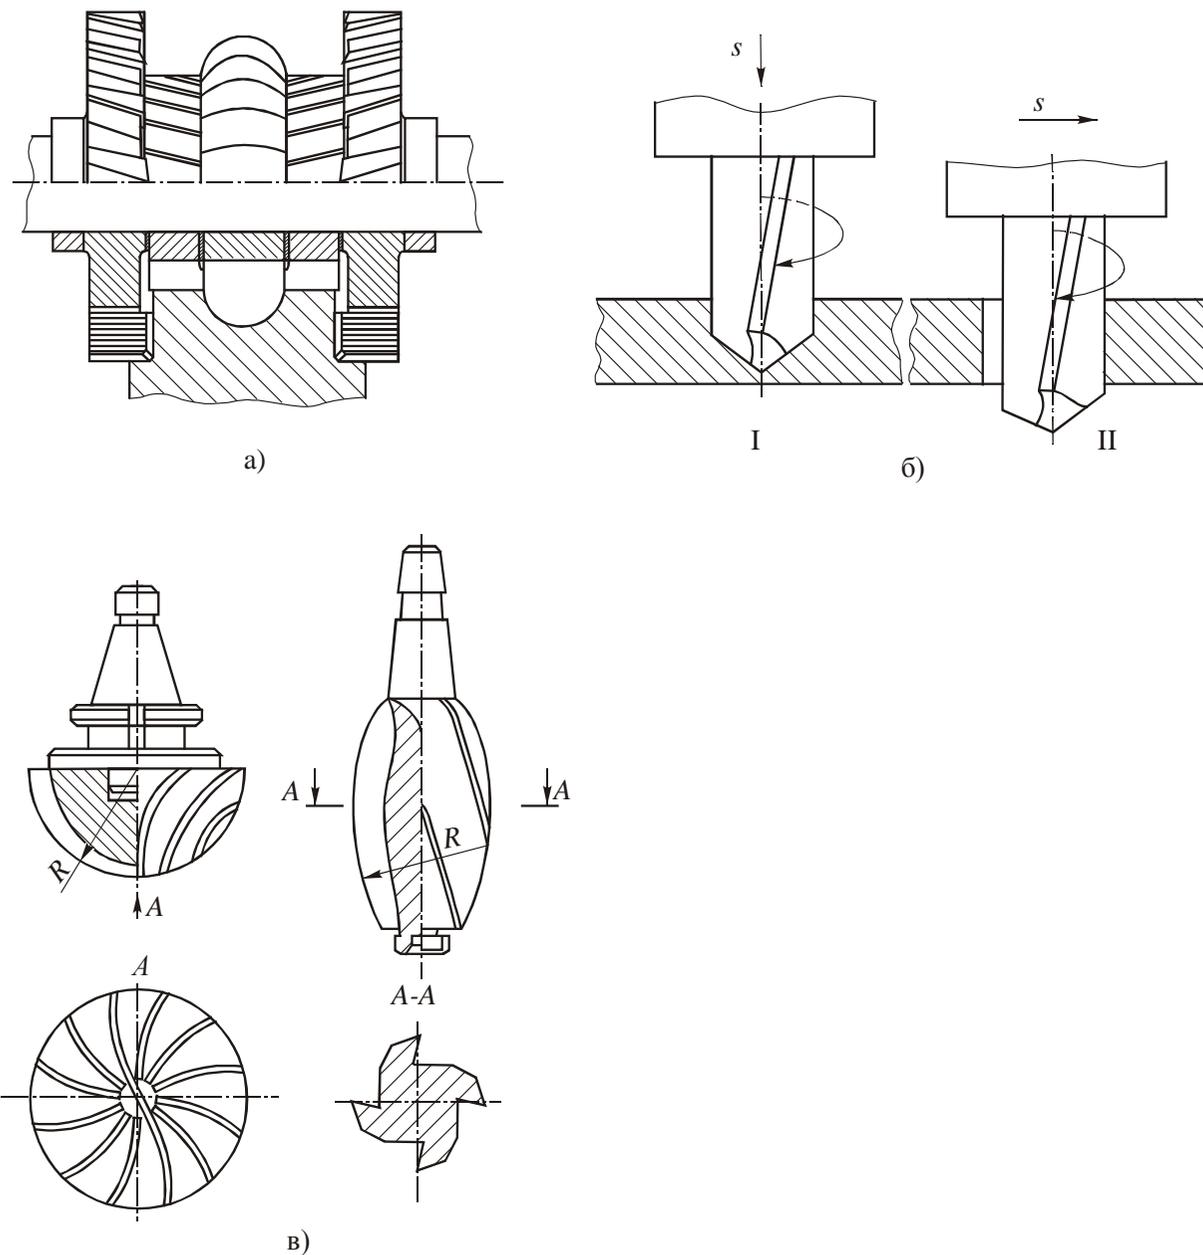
Фрезерные инструменты: *а* – набор фрез; *б* – фреза-сверло; *в* – фасонные фрезы для обработки сложных поверхностей
